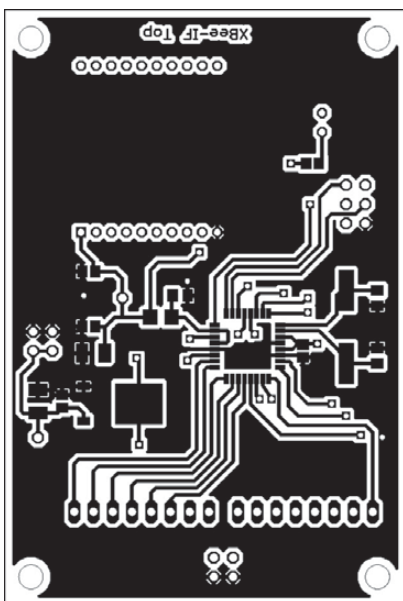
Layoutoberseite der Controllerplatine; Abmessungen 79 mm x 53 mm
